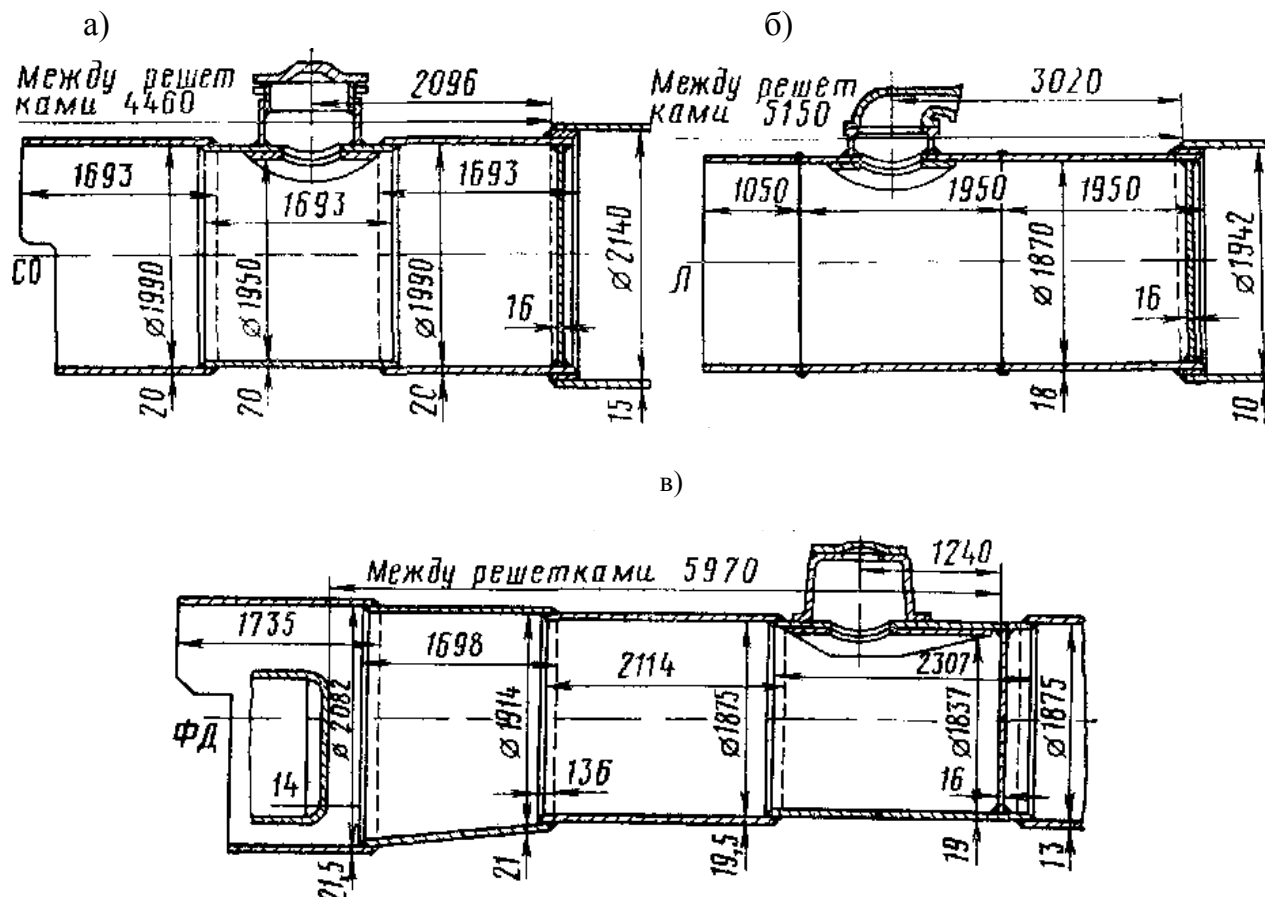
Типы соединения барабанов цилиндрической части котла паровозов: а – ступенчатый; б – сварной; в – телескопический
